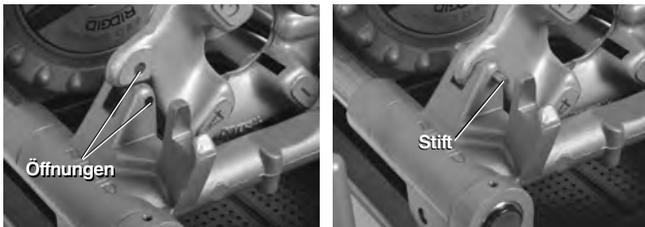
Halten des Linksgewindeschneidkopfs
